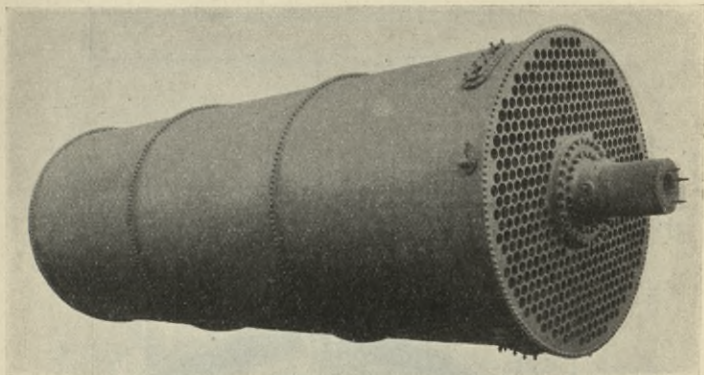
Röhrentrockner. (Maschinenfabrik Buckau A.-G.)
